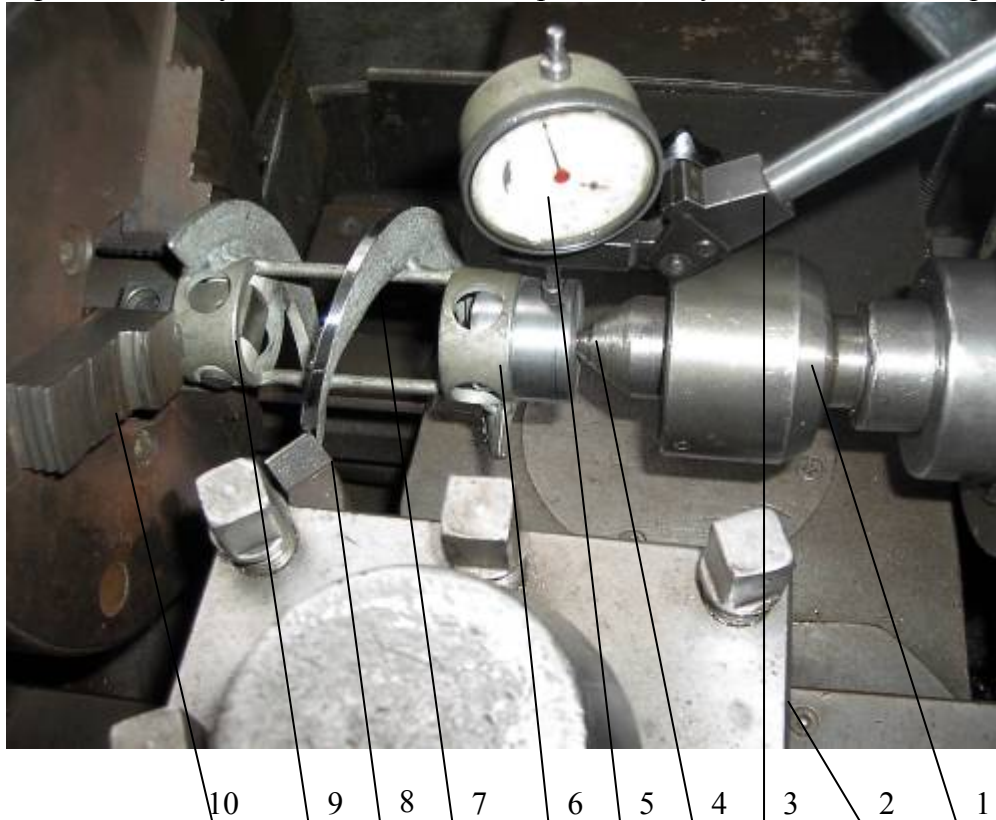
Експериментальна установка для проточування секції гнучкого гвинтового конвеєра: 1 – задній центр; 2 – супорт верстата; 3 – штанга індикатора; 4 – вставка; 5 – індикатор; 6 – права втулка; 7 – гвинтова спіраль; 8 – різець; 9 – ліва втулка; 10 – кулачок токарного патрона.
